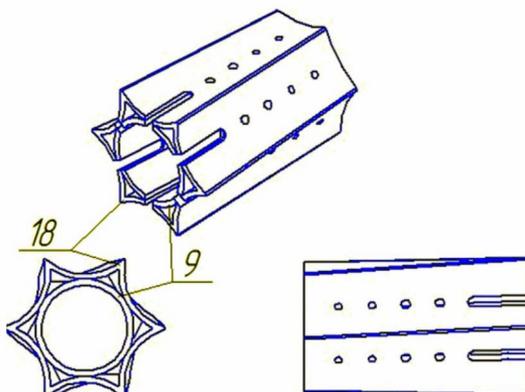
Полый барабан со звездообразным сечением и его трехмерная модель
